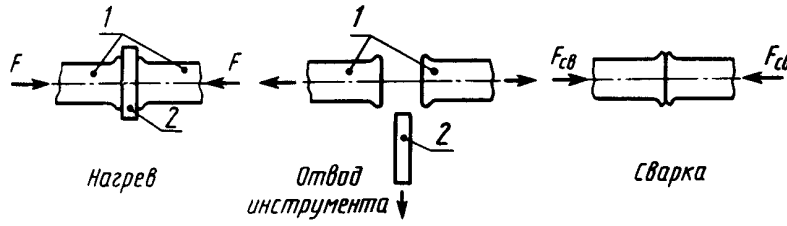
Схема контактной тепловой сварки нагретым инструментом
